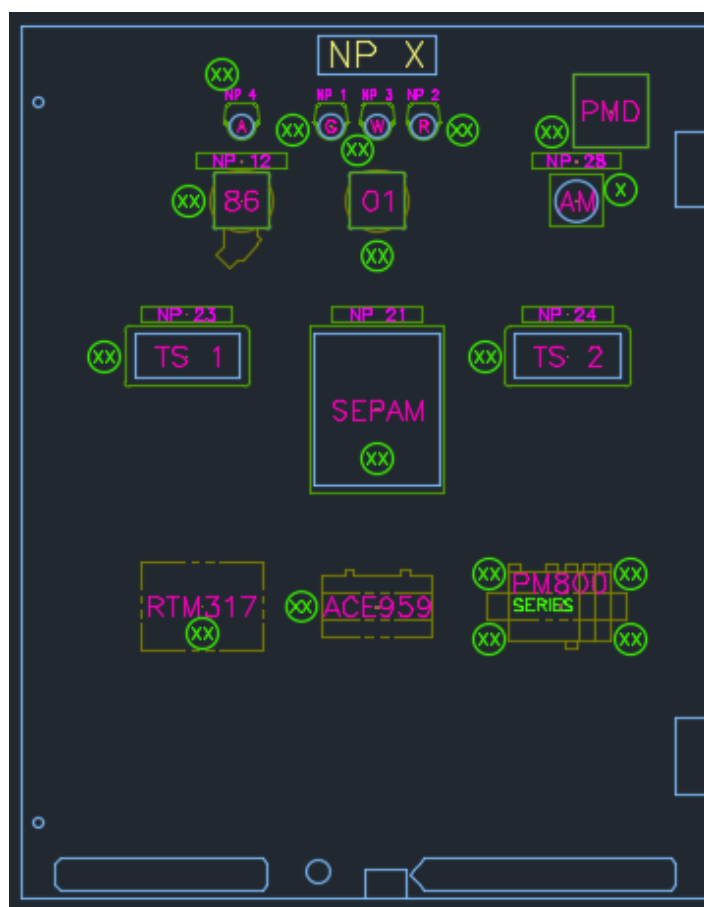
Plano de ingeniería del cableado de la puerta principal con componentes electrónicos. Fuente: Elaboración Propia.
